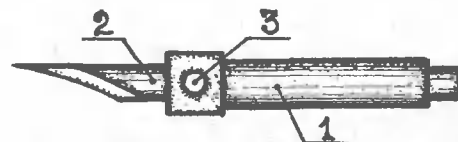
Сапожный нож для раскройки кожи на верха обуви и подкладки.
